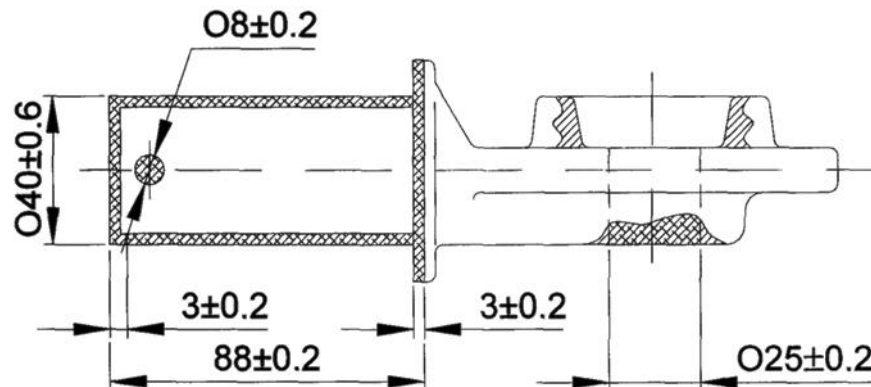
Заготовка опори з призначеними припусками і допусками
